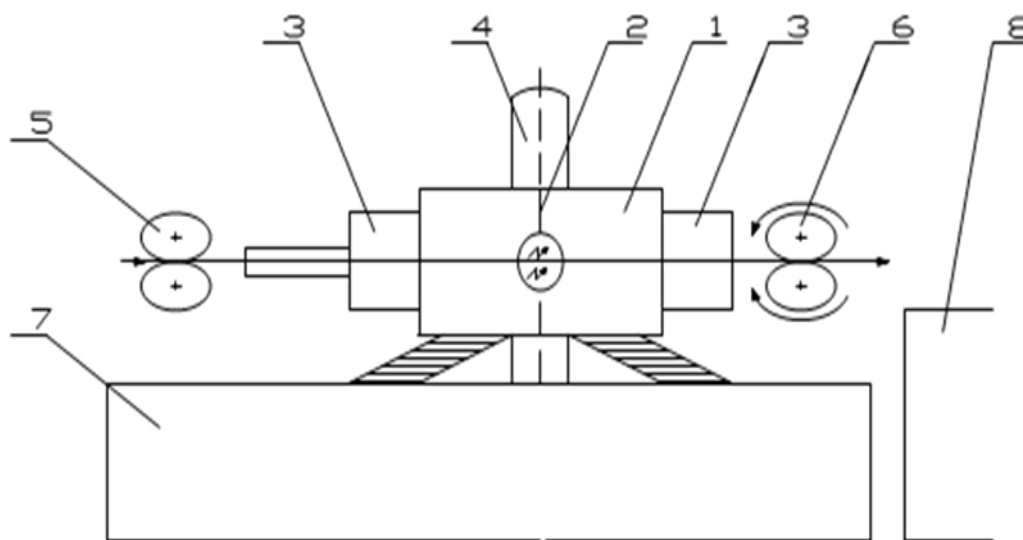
Схема устройства для ЭПО металлопроката:
